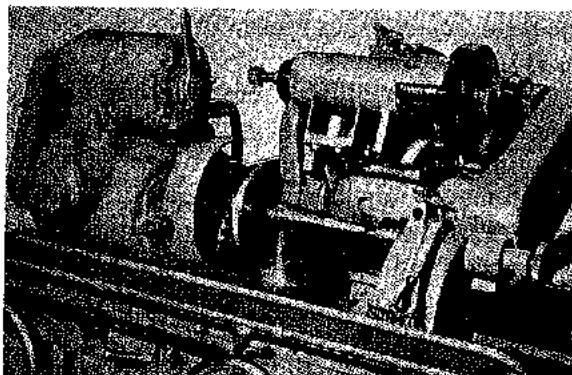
Rectificado de un cono (Cincinnati Milling Machine Co.)
